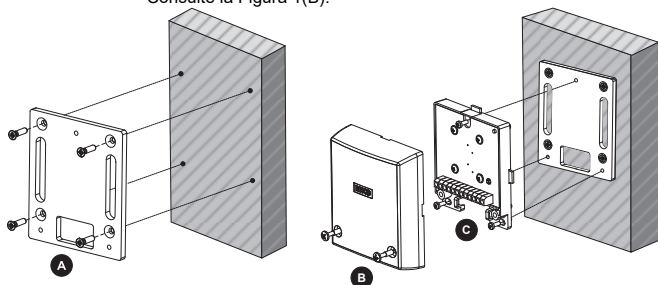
Montaje del detector con la placa de montaje. (Nota: Fije la placa de montaje utilizando tornillos de fijación o, si lo desea, soldando la placa a una superficie metálica.)
